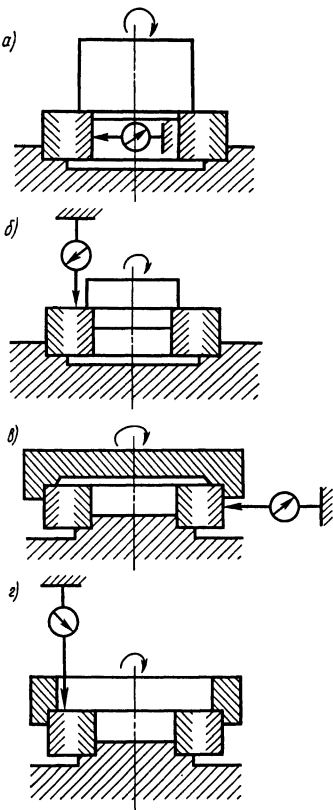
Схемы проверки радиального (а и б) и осевого (в и г) биения внутреннего и наружного колец подшипника
